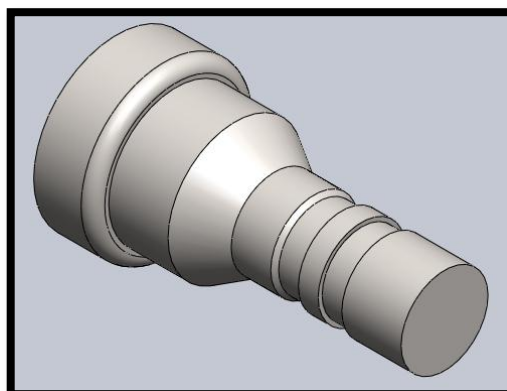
Diseño de la pieza de torneado en SolidWorks.
